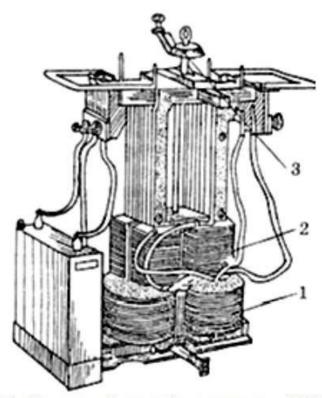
Сварочный трансформатор типа ТСК-500
